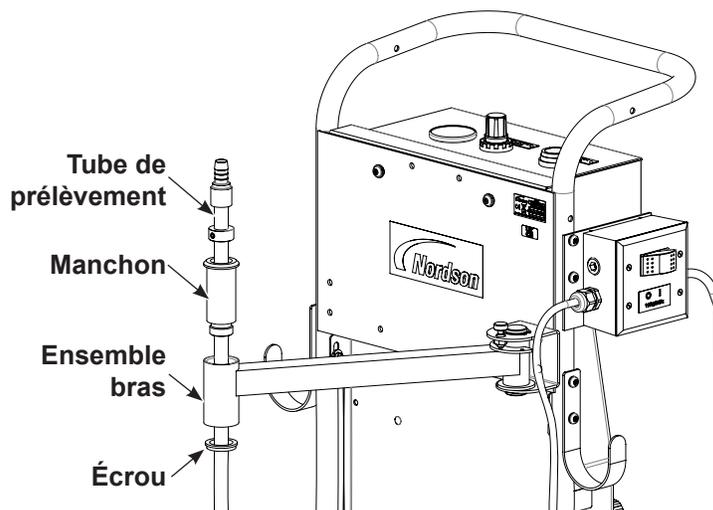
Installation du tube de prélèvement dans l'ensemble bras
